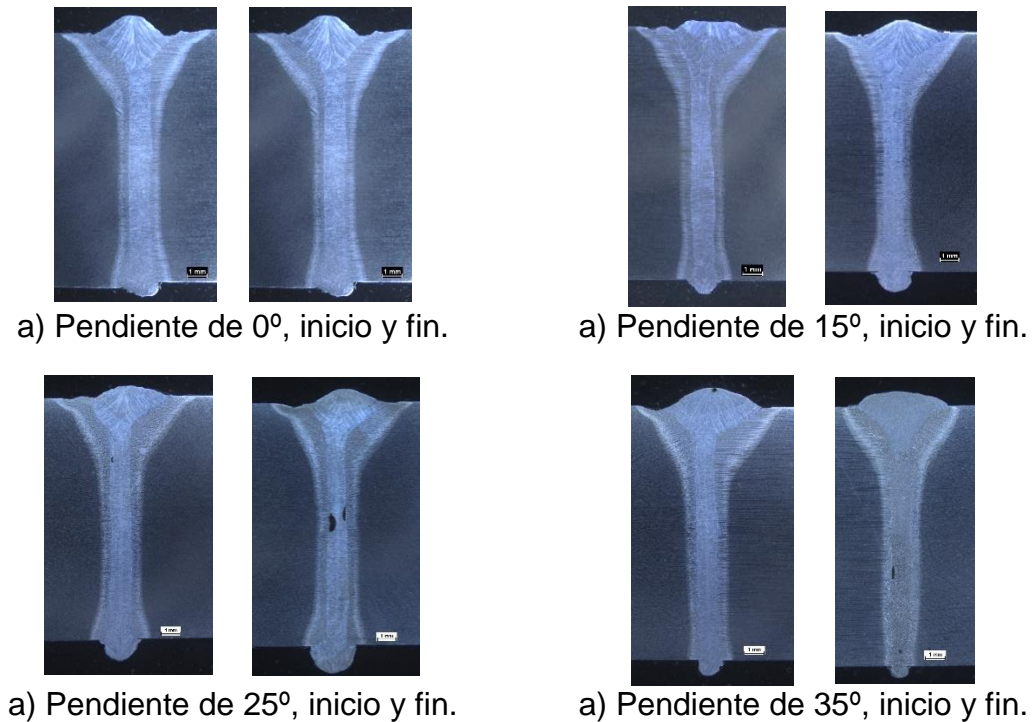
16. Sección transversal para cada cupón soldado por el proceso HLAW.
